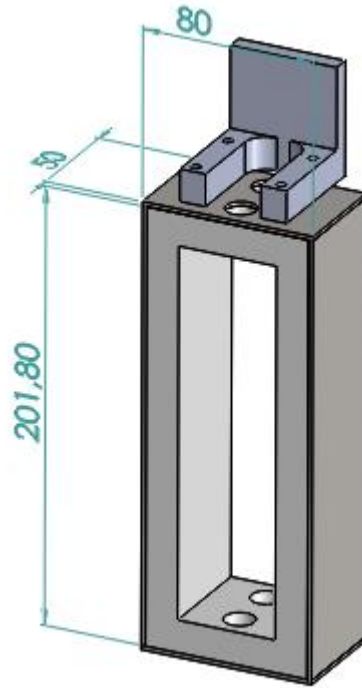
Desenho 3D em SolidWorks do suporte de lâmpadas e respectivas dimensões exteriores.
